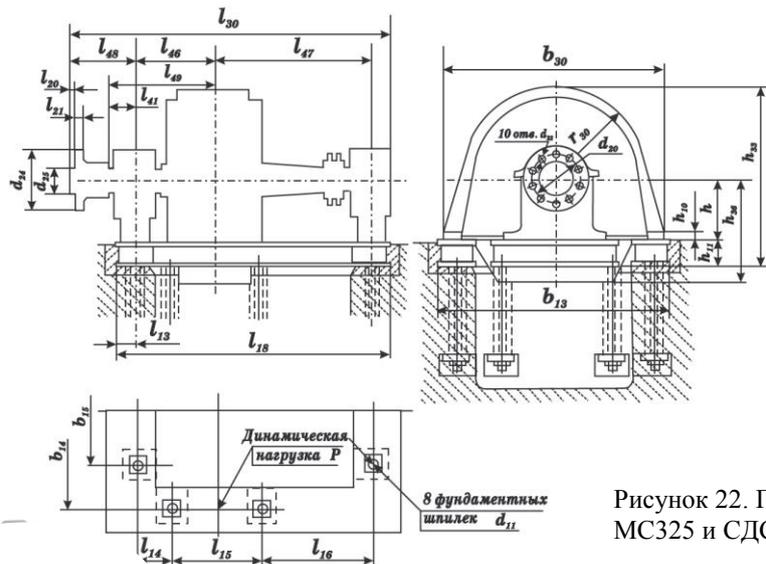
Габаритные размеры МС325 и СДСЗ-290
